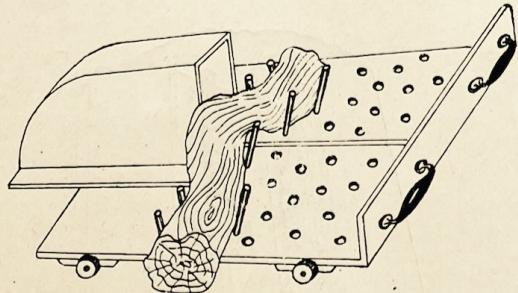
Još jedna vrsta naprave za potiskavanje
